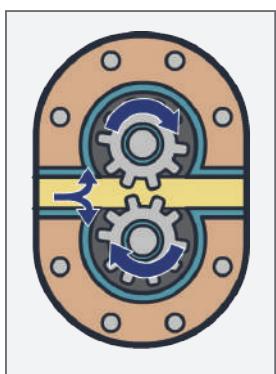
Bomba de pressão de óleo tipo engrenagem
